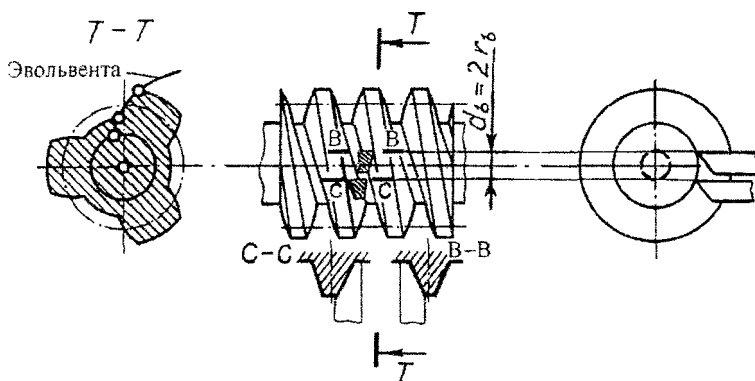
Эвольвентный червяк ZJ и схема установки резцов для нарезания витков правого направления
